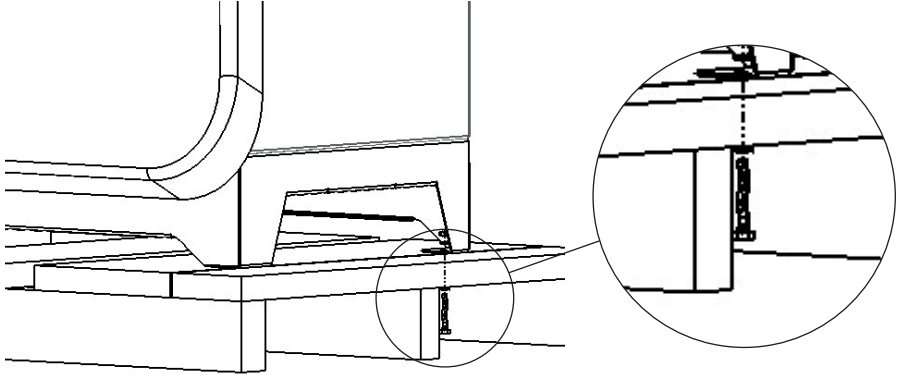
Entfernen der Transportsicherung - Herausdrehen der Befestigungsschrauben
